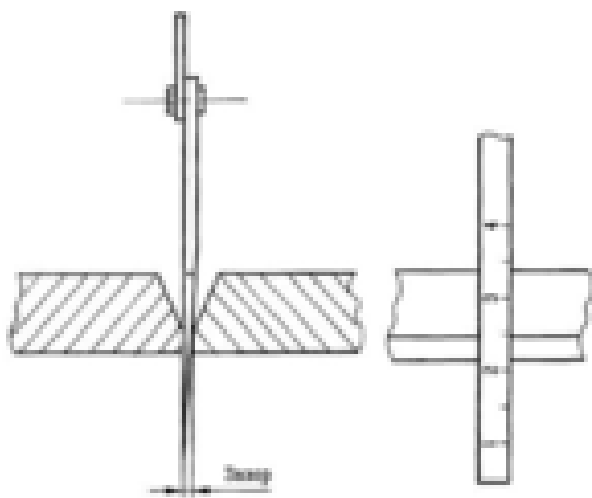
Схема измерения зазора сварного шва
